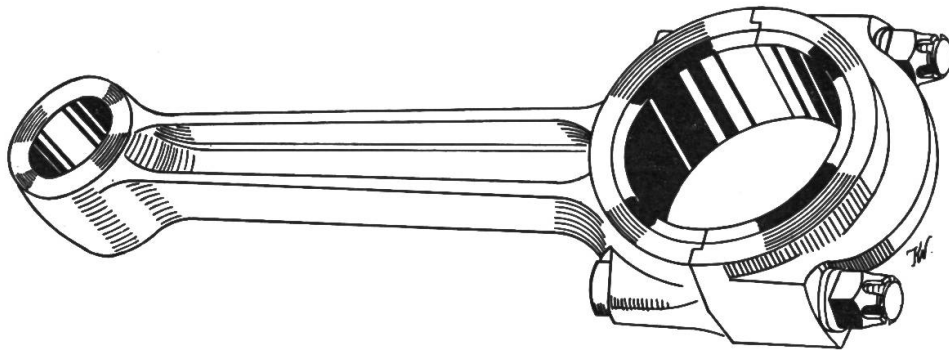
Kräftig dimensionierte Pleuelstange eines Dieselmotors («Buda»).
